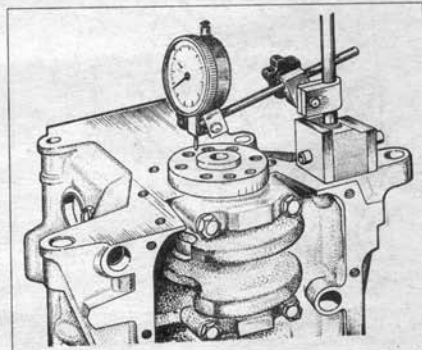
Проверка осевого свободного хода коленчатого вала
